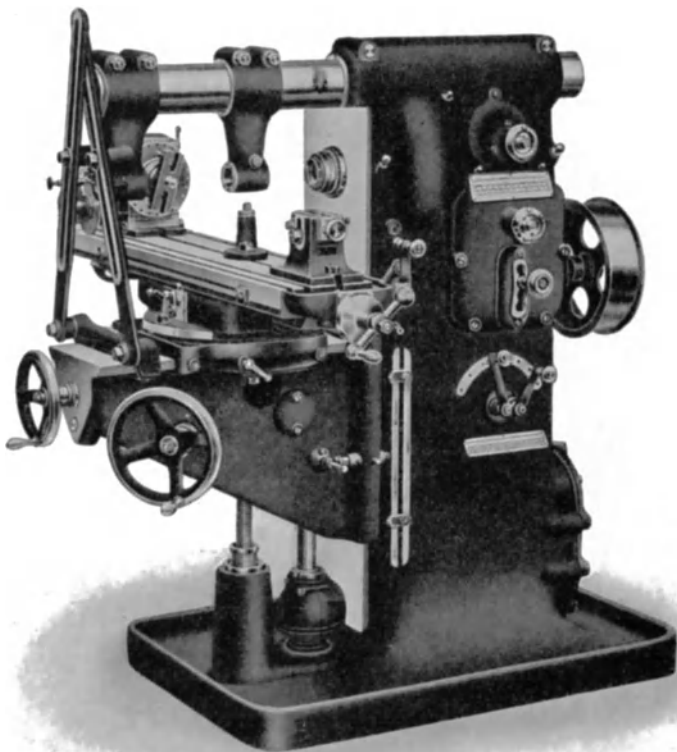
Die Universalfräsmaschine der Wanderer-Werke.
